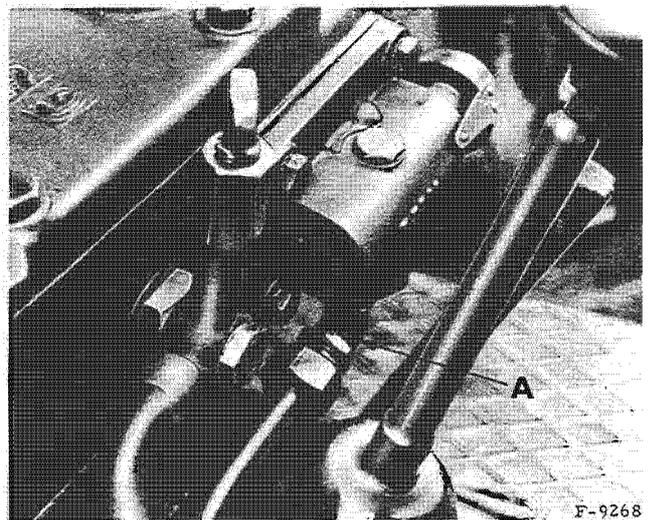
Assemblage tuyauterie - raccord coudé.
